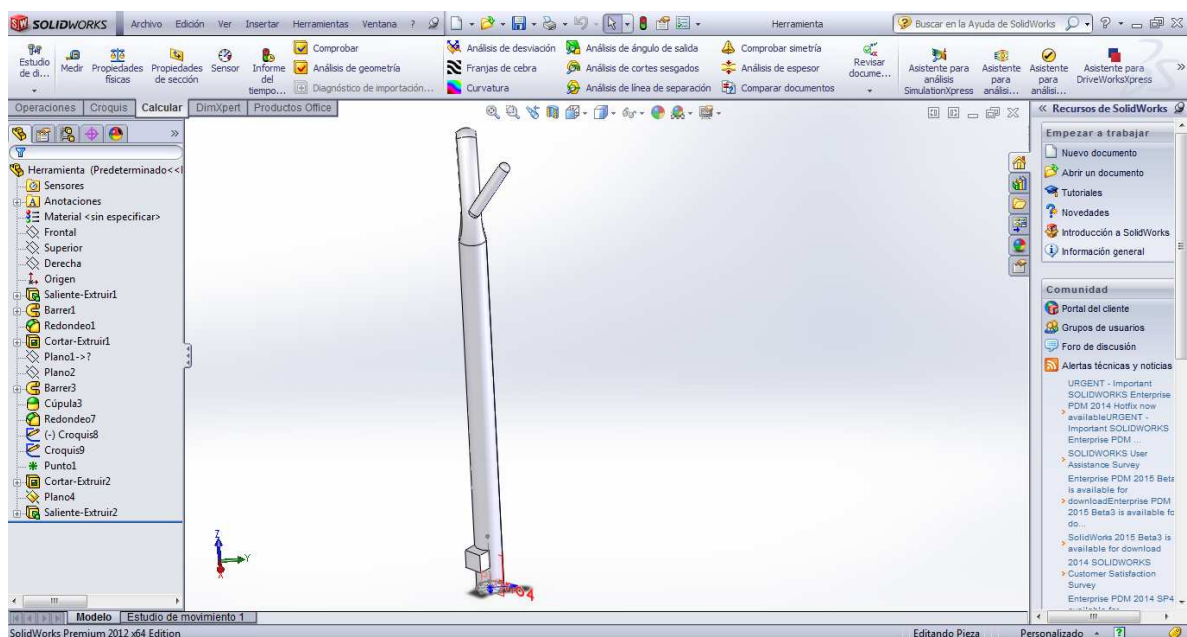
Vista 2 del conjunto parte metálica+acelerómetro en SOLIDWORKS
